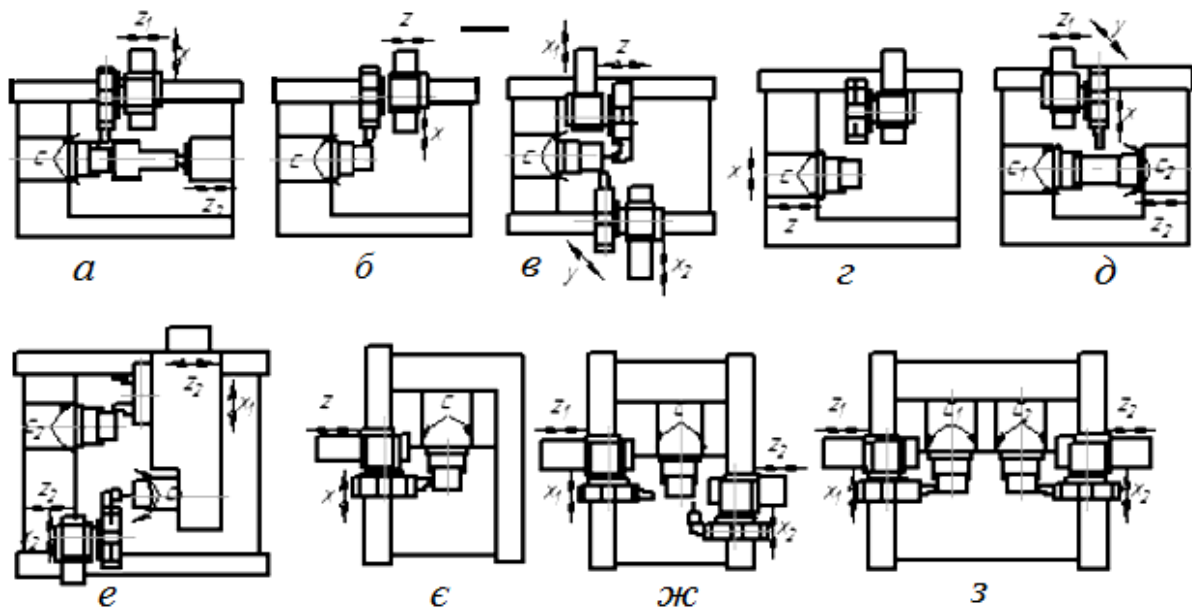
Схеми компоновки верстатів токарної групи з горизонтальною віссю обертання шпинделя
